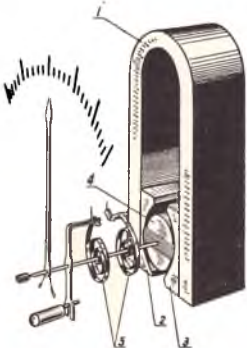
Устройство прибора магнитоэлектрической системы: 1 — постоянный магнит; 2 — полюсные вантачечники; 3 — рамка с обмоткой; 4 — внутренний цилиндр магнитопровода; 5 — пружины
